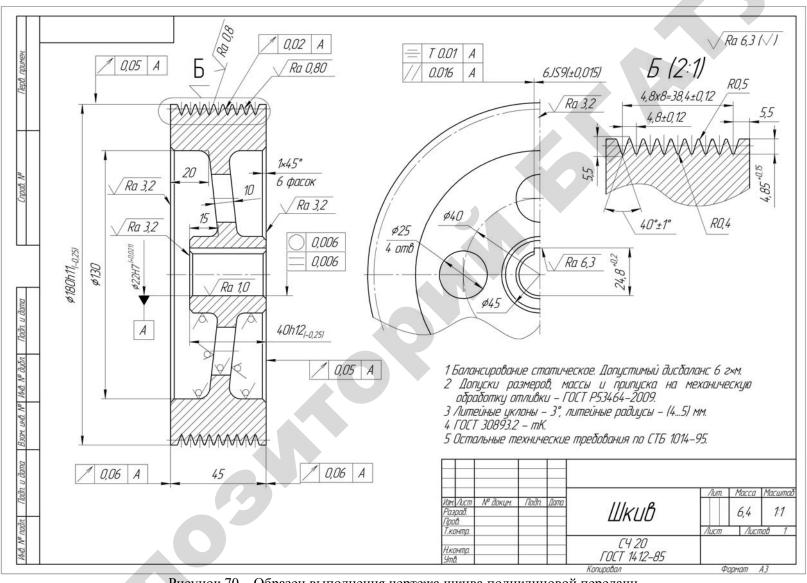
Образец выполнения чертежа шкива поликлиновой передачи
